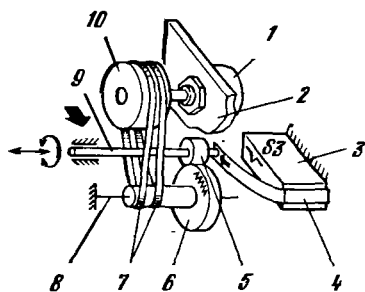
Верньерное устройство автомагнитолы «Гродно 208-стерео»: 1 — резистор СПЗ-4аМ; 2 — крошфейн; 3 — микропереключатель; 4 — пружина; 5, 6 — колеса зубчатые; 7 — пассик; 8, 9 — вал; 10 — шкив
